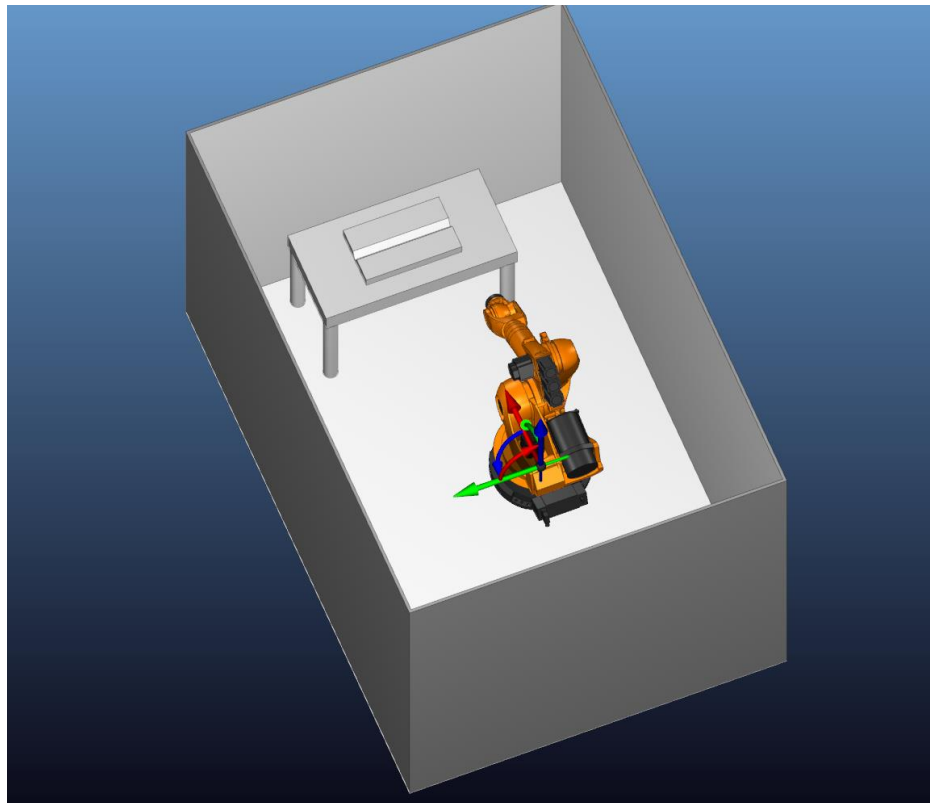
10 Representación del robot dentro de la celda de soldadura
